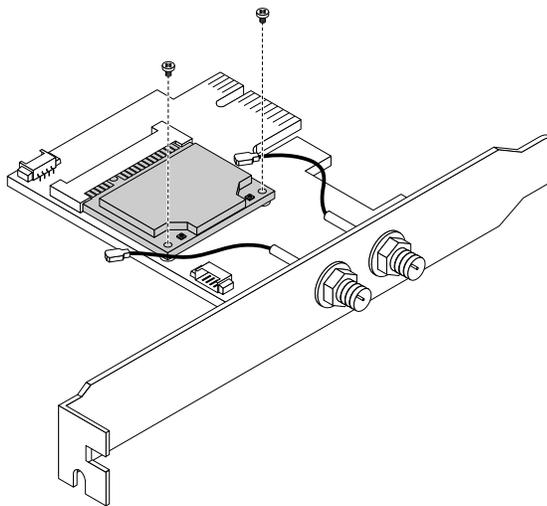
Die Schrauben zur Befestigung des Wi-Fi-Kartenmoduls anbringen
